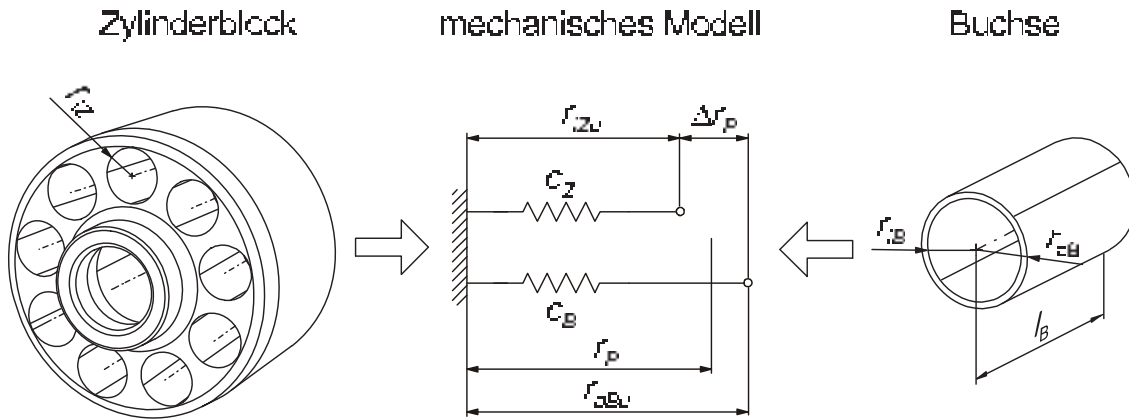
Zylinderblock (links), Buchse (rechts) und mechanisches Ersatzmodell zur Auslegung des Presssitzes.
